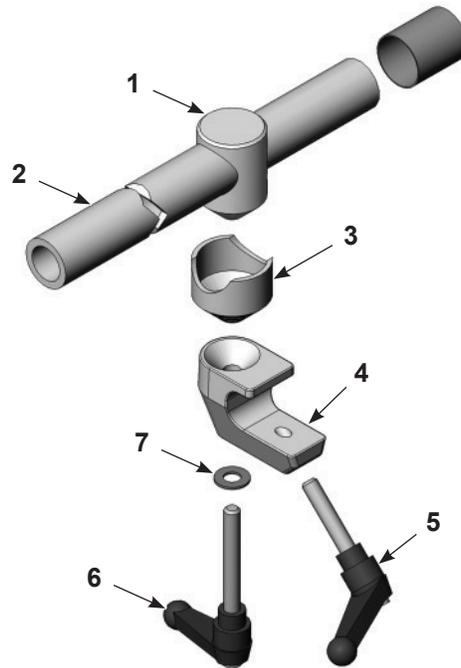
Barra de pistola de aplicación para pistolas de aplicación de montaje en barra
